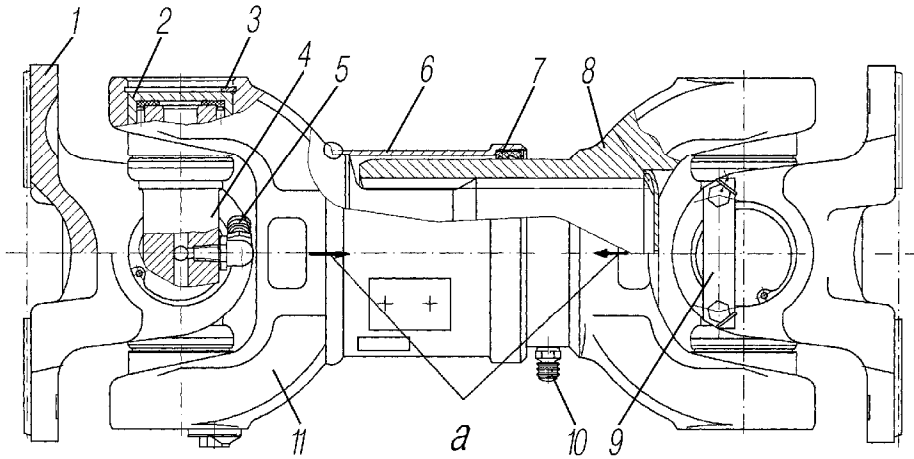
Вал карданный промежуточный с торцевыми шлицами:
